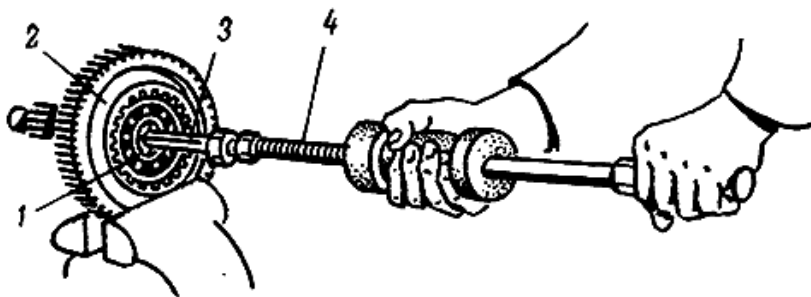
Выпрессовка подшипника из вторичного вала: 1 — подшипник; 2 — вторичный вал; 3 — цанга; 4 — инерционный съемник
